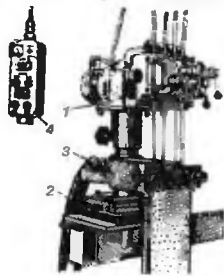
Апарат А-1304 для електрошлакового зварювання плавким мундштуком:
